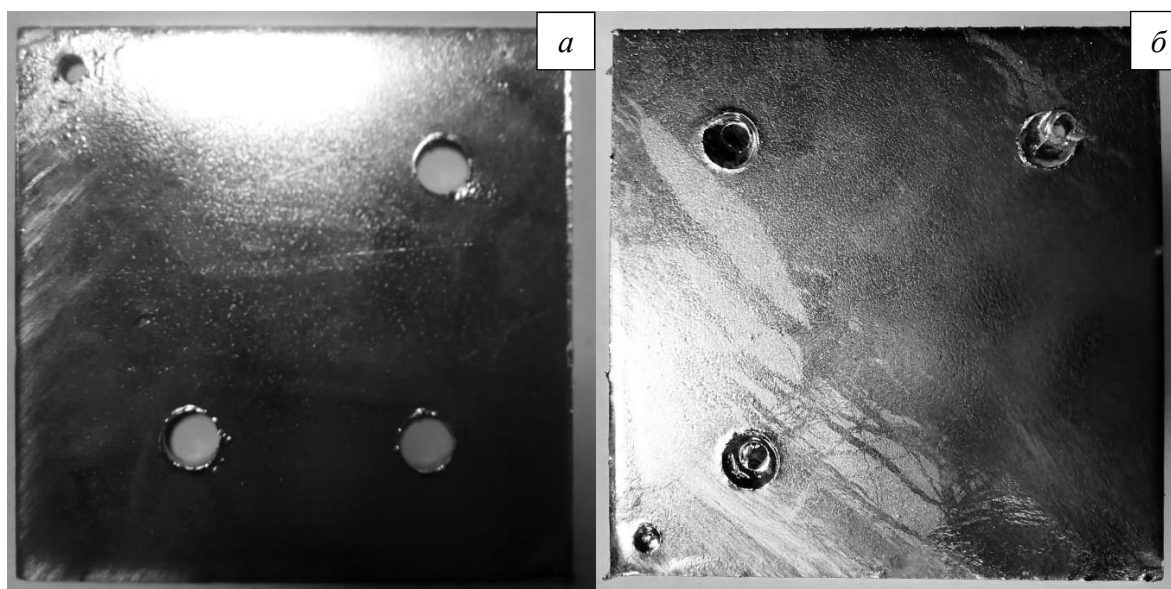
Оцинкованный образец с чистыми отверстиями (а) и с затянутыми цинковой пленкой (б)
